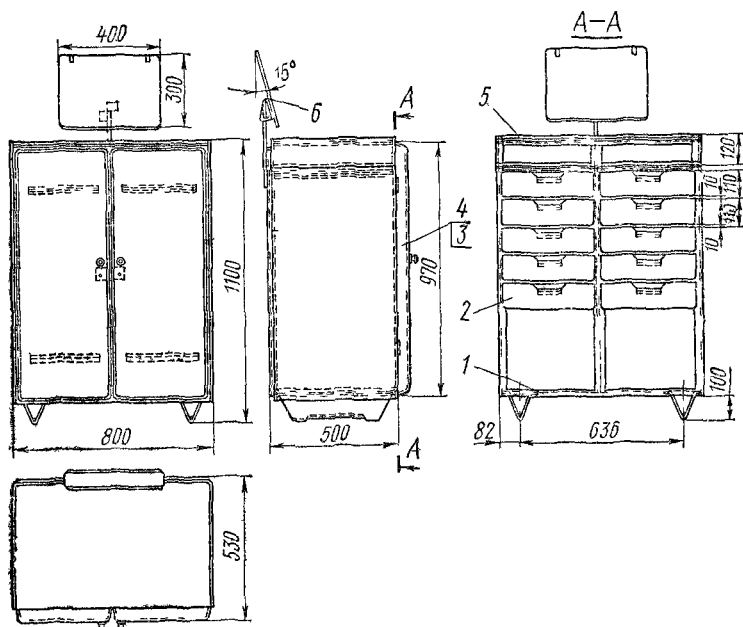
Тумбочка инструментальная для двухсменной работы:
